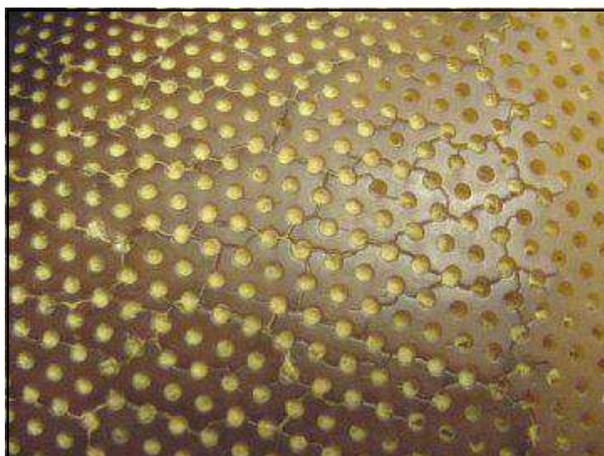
La severidad de las grietas en el lado de la manta puede ser reducida con la indexación de la manta.
